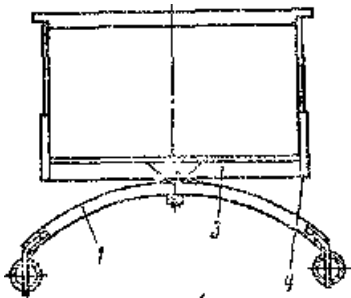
Приспособление для крепления ульевой рамки на грузозахватных вилах универсальной тележки-подъемника
